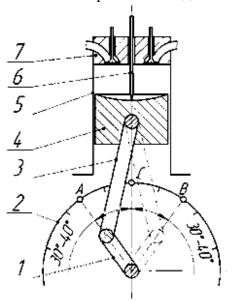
Определение мертвых точек 1 - Коленчатый вал; 2 - Маховик; 3 - Шатун; 4 - Поршень; 5 - Цилиндр; 6 - Металлический стержень; 7 - Крышка цилиндра
